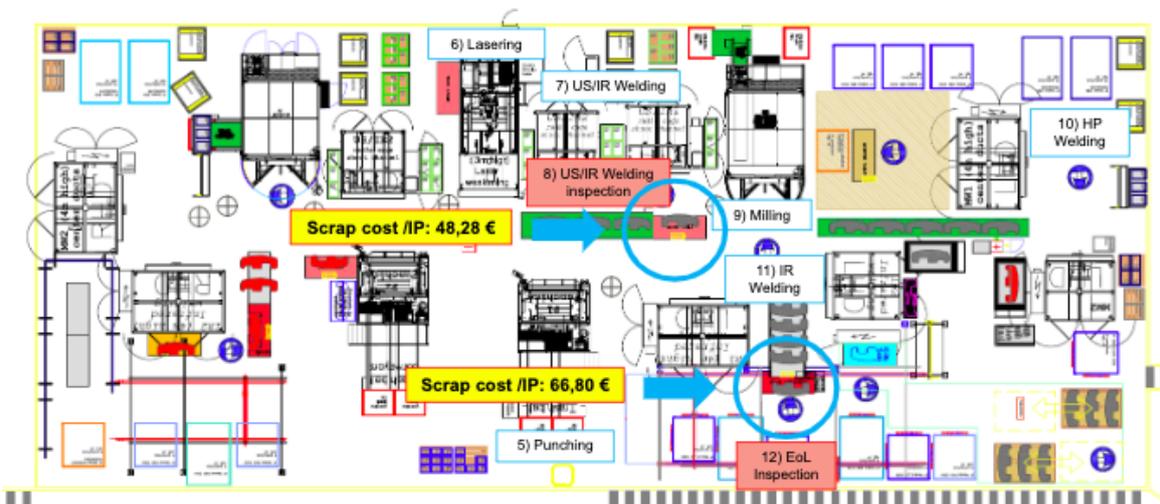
Layout de la línea de producción de soldadura del IP.
